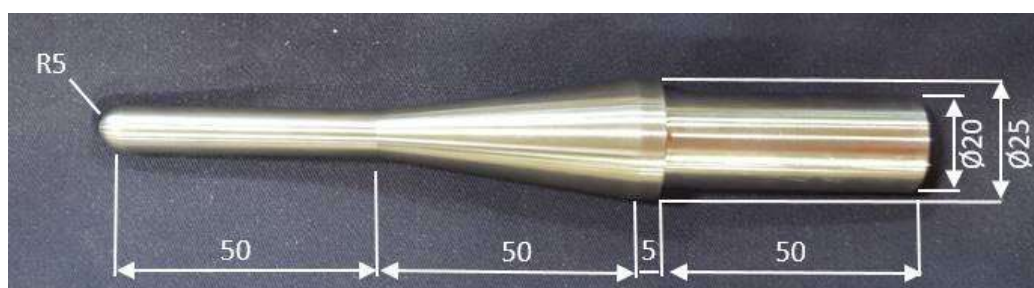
Ferramenta utilizada e suas principais dimensões em milímetros.
